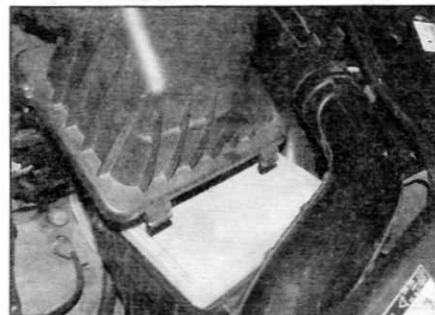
, б. ... высвободите два выступа и снимите крышку с корпуса воздушного фильтра (модели с двигателем 2.0 л)
